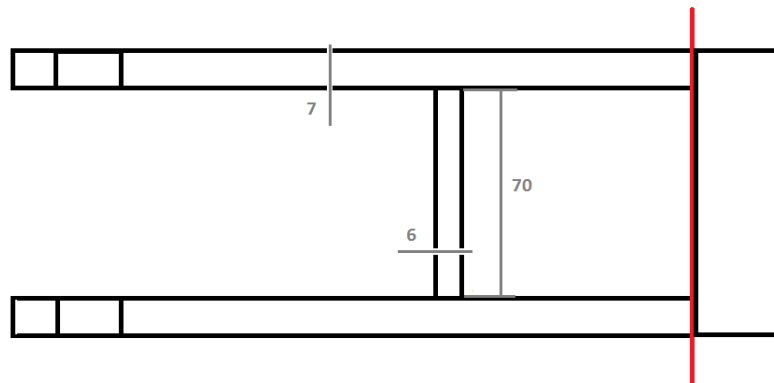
Alzado del tramo anclado del brazo, cotas en mm.
